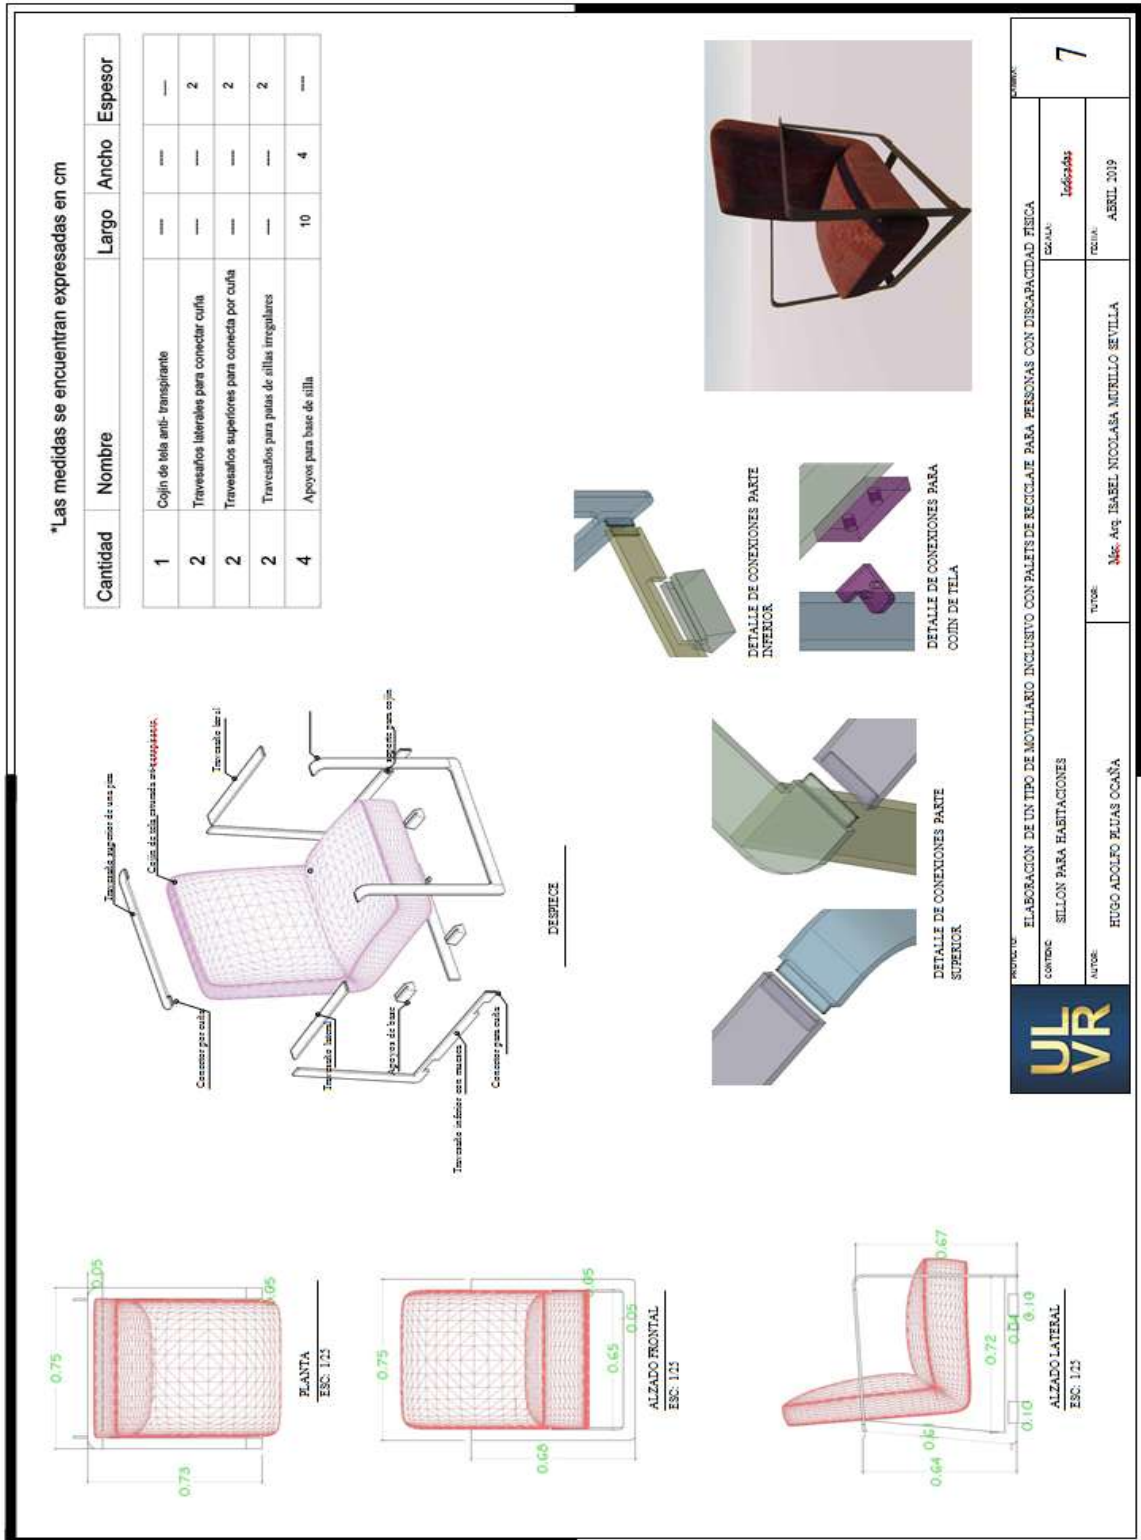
Diseño sillón para habitación, vista y medidas
